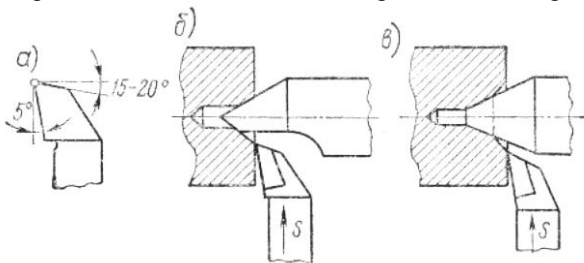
Геометрия подрезного резца и способы формирования торца при использовании полуцентра и 3-х конусного центрового отверстия
